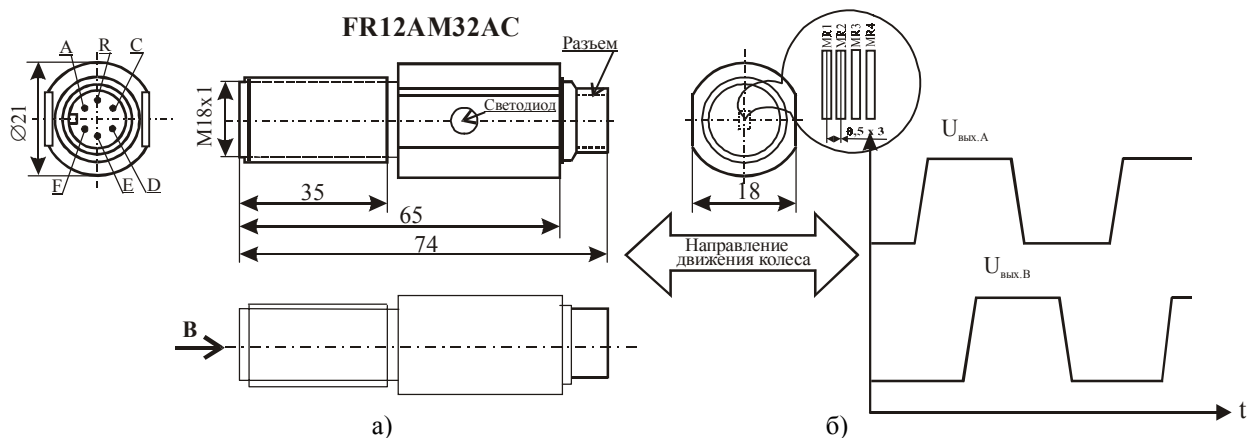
Внешний вид и габаритные размеры (а) и вид сигнала на выходе (б) для датчика типа FR12AM32AC
